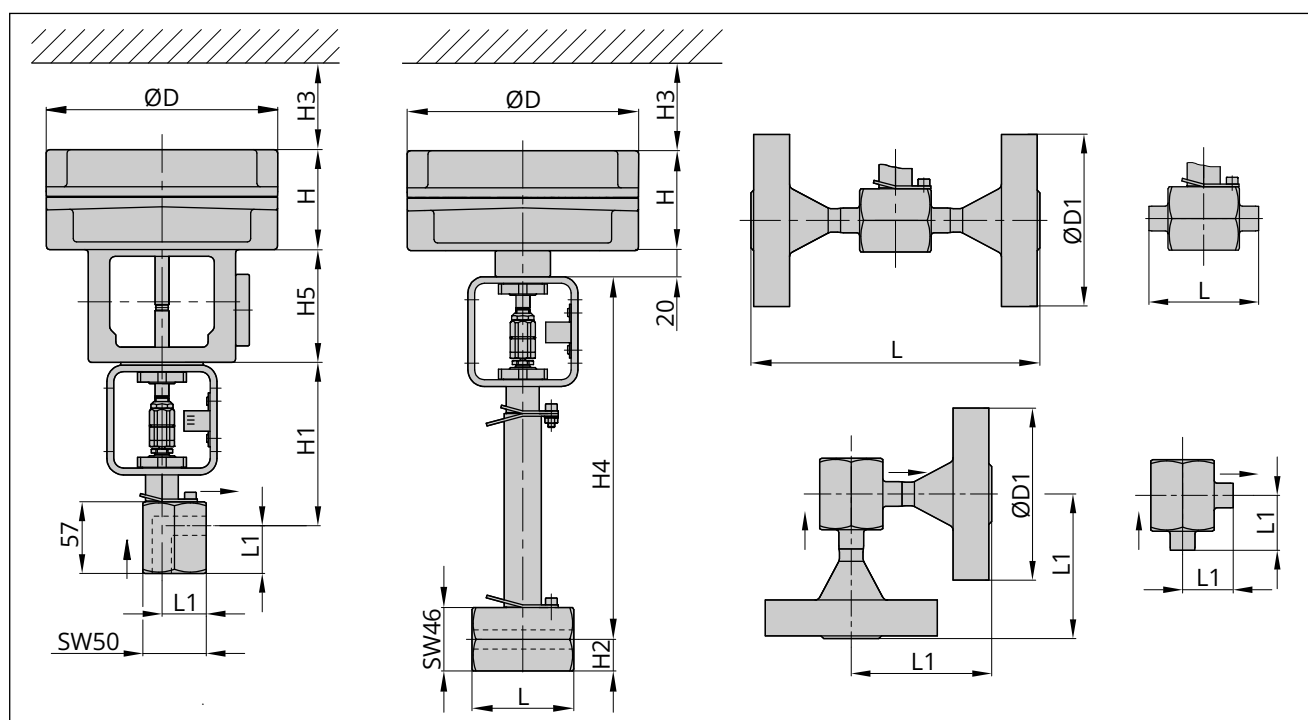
von links nach rechts: Typ 3510-7 Eckventil mit Innengewinde, Typ 3510-1 Durchgangsventil mit Innengewinde und Balg-/Isolierteil, Typ 3510 Gehäuseausführung mit Flanschanschluss, Typ 3510 Gehäuseausführung mit Anschweißenden
